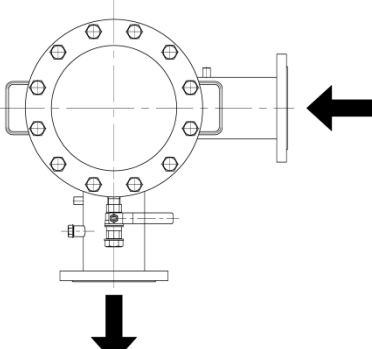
Габаритные размеры фильтров газовых «РЕД»
